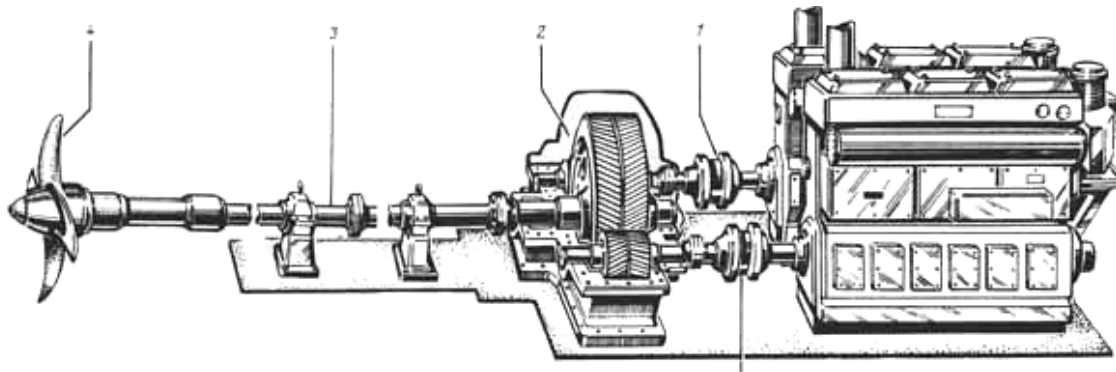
Дизель-редукторна енергетична установка з двома середньоборотними дизелями: 1 – муфти; 2 – редуктор; 3 – валопровід; 4 – гребний гвинт
